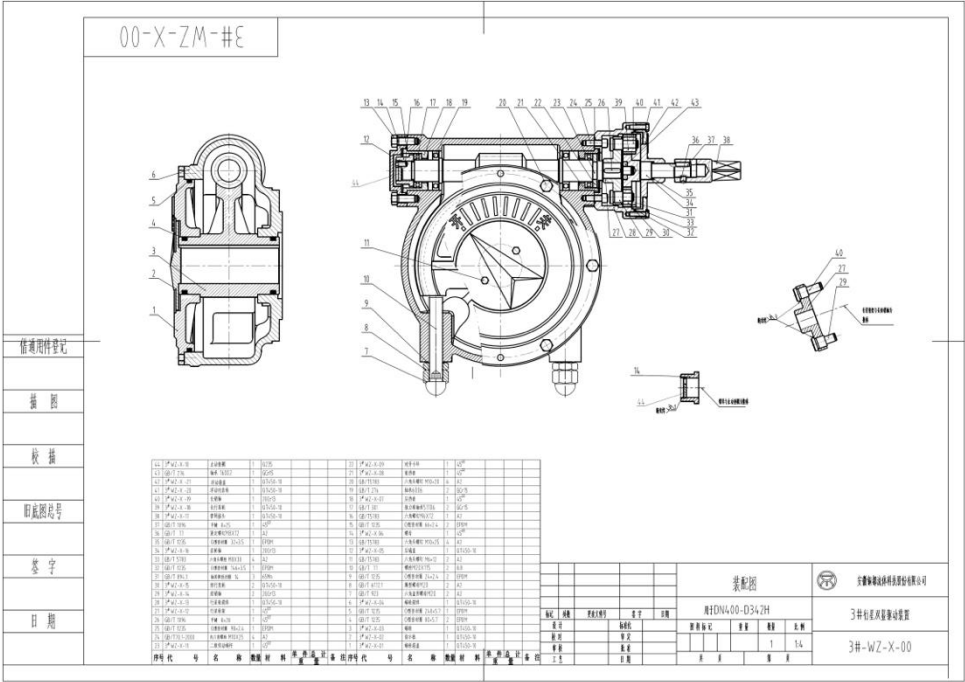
DN400 金属硬密封蝶阀手动驱动装置装配图
